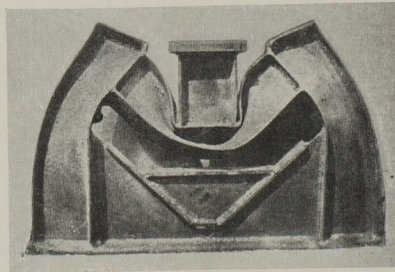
Geschweißte Eisenkonstruktion nach dem Biegeversuch, ohne Anriß in den Schweißnähten
